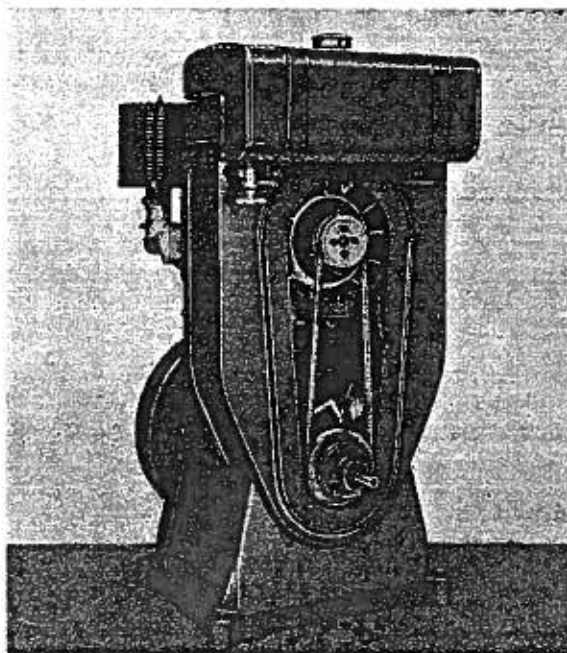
Dépose du carter mobile de la calandre du radiateur.
